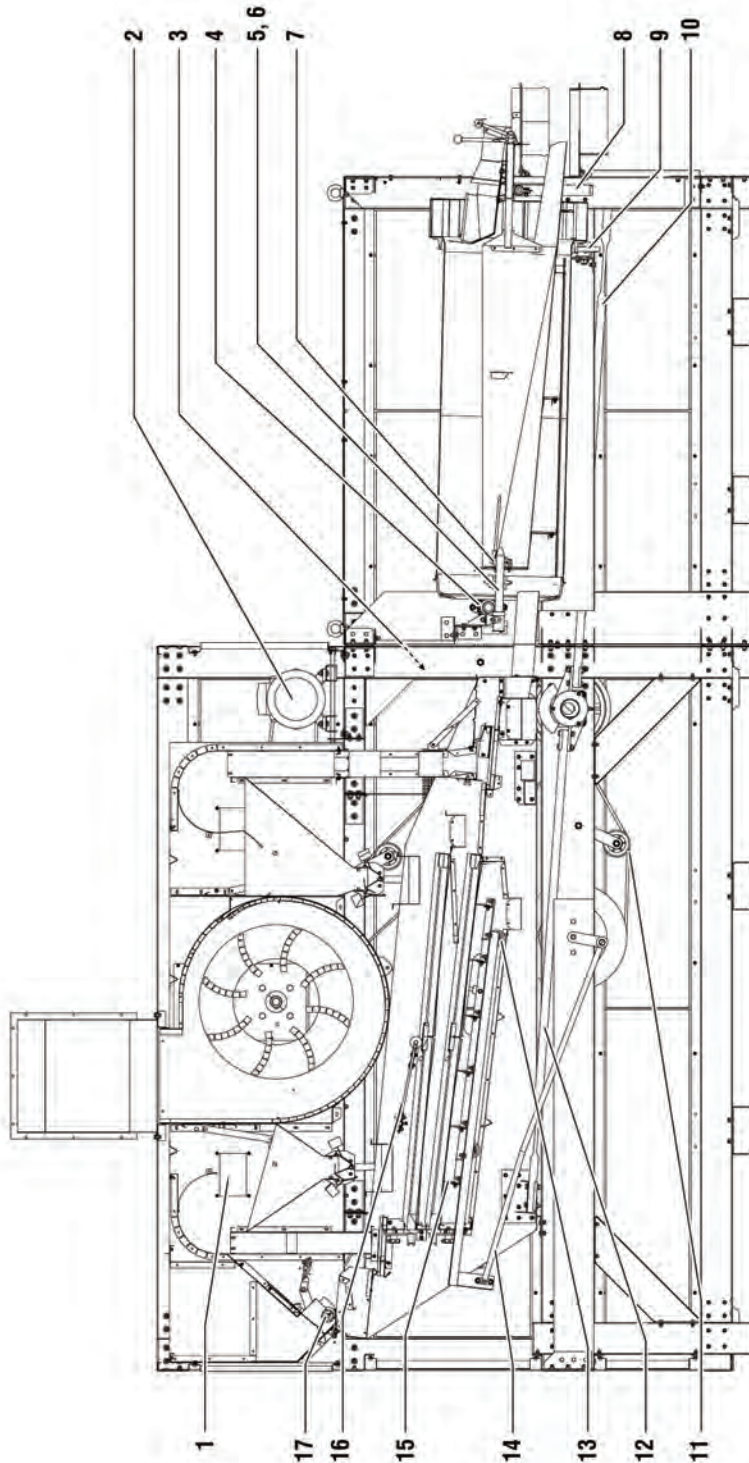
Места расположения запасных частей и быстроизнашивающихся деталей
